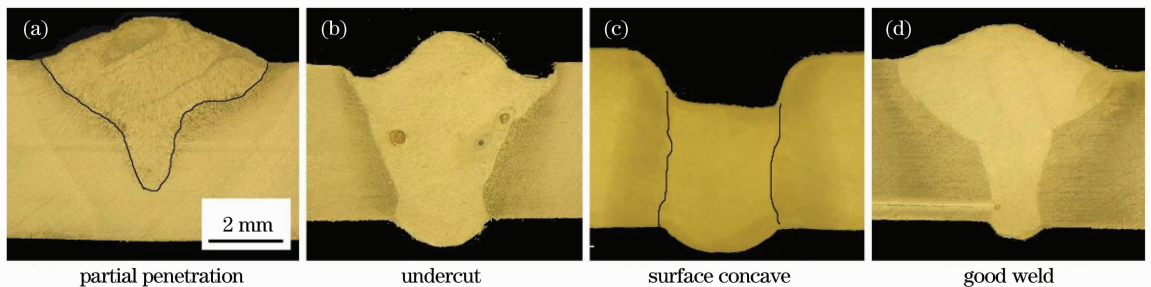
焊接速度不当时焊缝缺陷及良好焊缝的截面形貌
